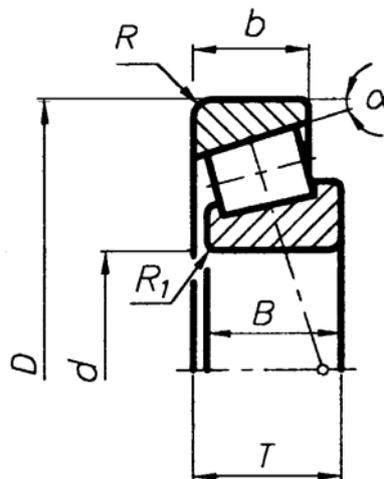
Габаритные размеры роликовых конических однорядных подшипников
